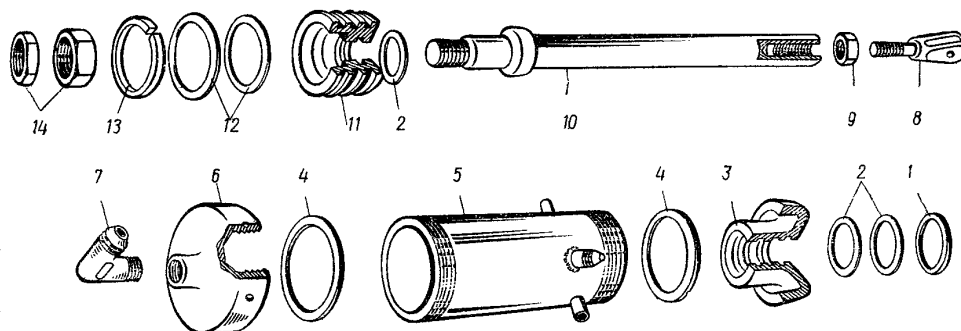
Типовой пневматический цилиндр управления клапаном и тормозом:
